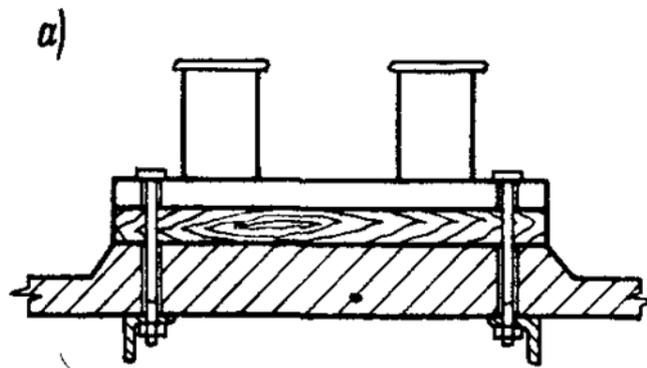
Крепление кнехта к корпусу сквозными болтами
